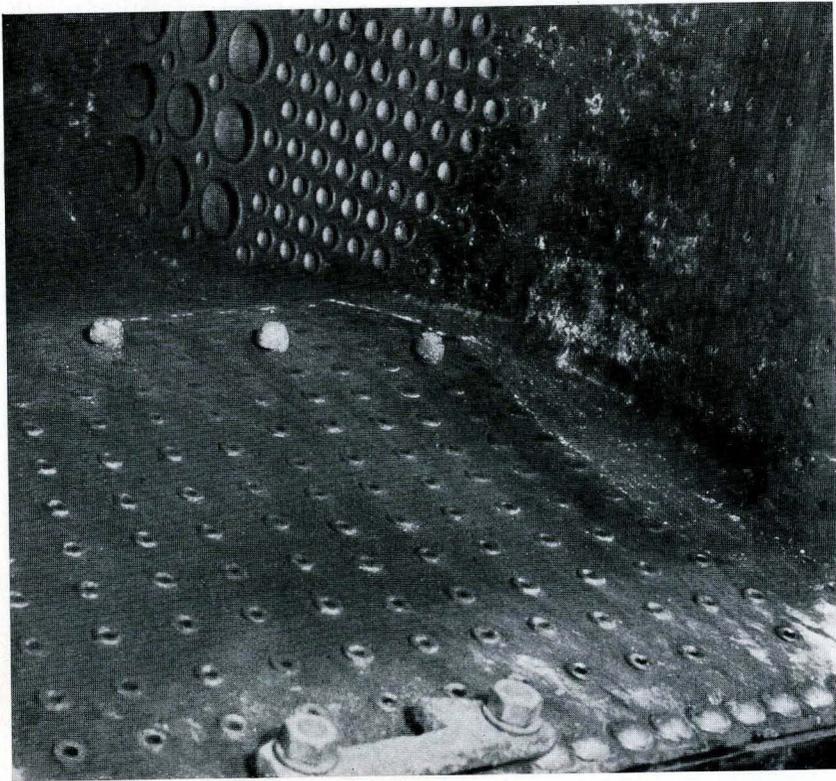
Inneres einer kupfernen, vollständig geschweißten Feuerbüchse. Seitenwand aus Kuproduer. Die kupfernen Stehbolzen in der Rohrwand sind autogen eingeschweißt (Sebaldsbrück)
